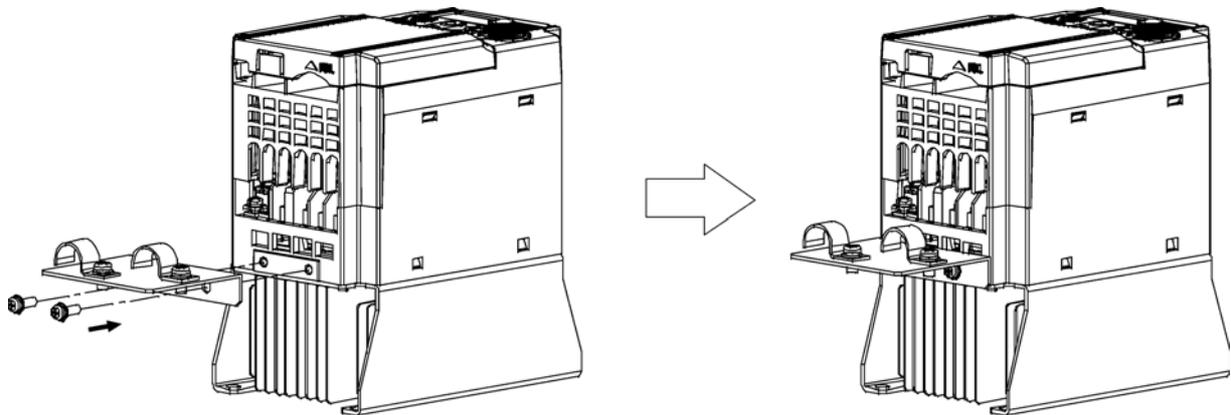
Fissaggio della flangia della messa a terra EMC
